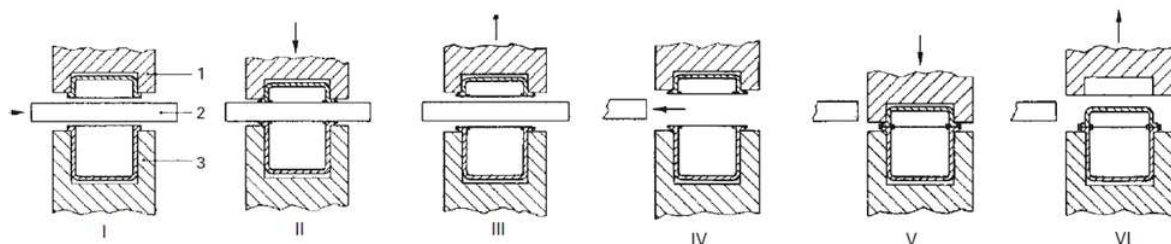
Ablauf Hitzeelementschweißen [13]
